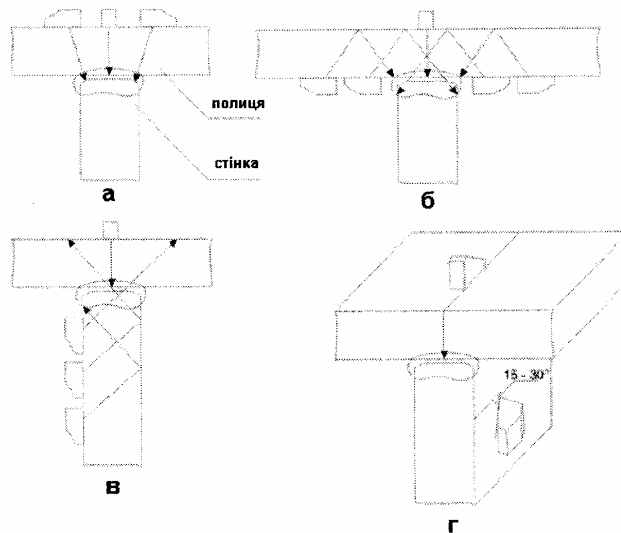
Схемы контроля сварных соединений клейм.
